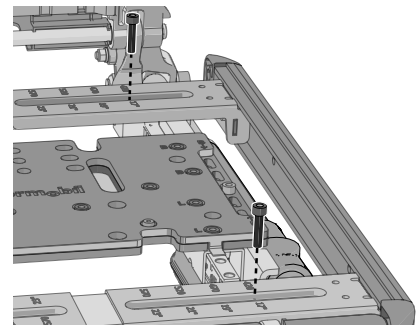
Die UniTrack-Schienenhalterungen werden mit zwei Schrauben befestigt.
